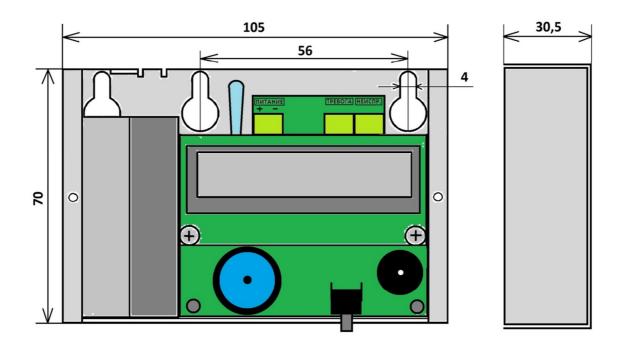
Габаритные и установочные размеры сигнализатора ДГ-3-У
